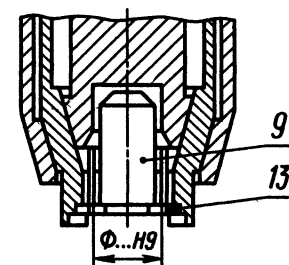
Захватное устройство и схемы сборки шестеренчатых насосов
